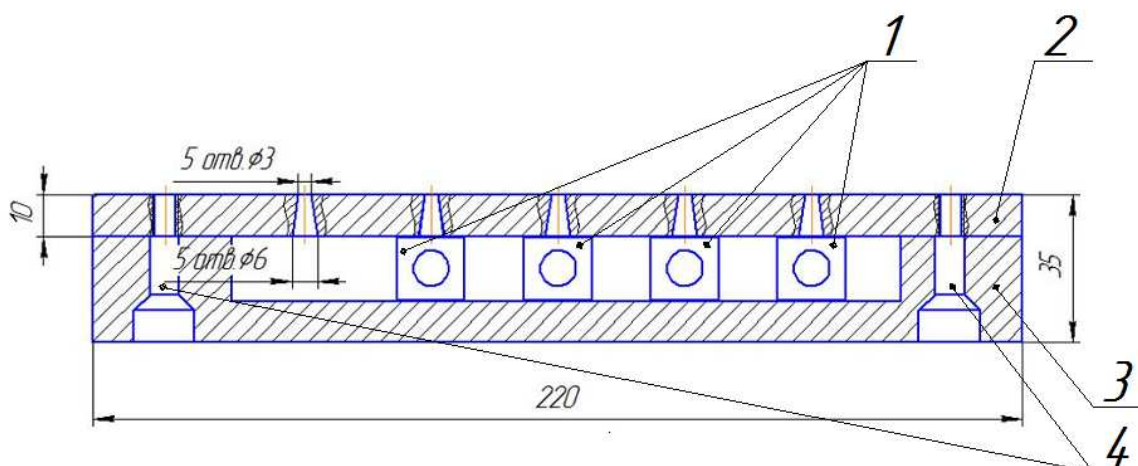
Блок-образец. 1 – Штифты; 2 – Поверхность для нанесения покрытия; 3 – корпус; 4 – Винты.
